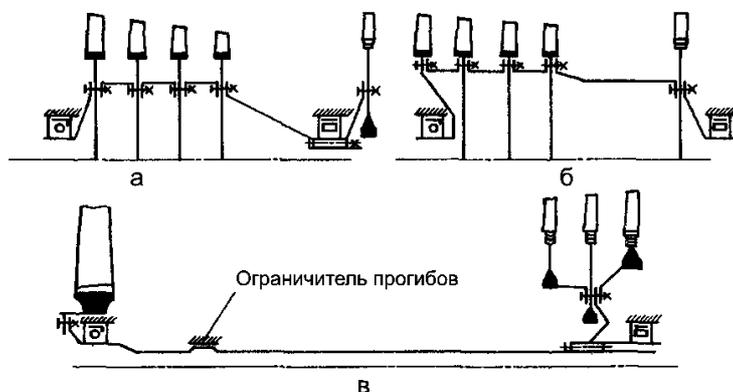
Схемы двухопорных роторов с передним (а) и задним (б, в) расположением подшипника турбины
